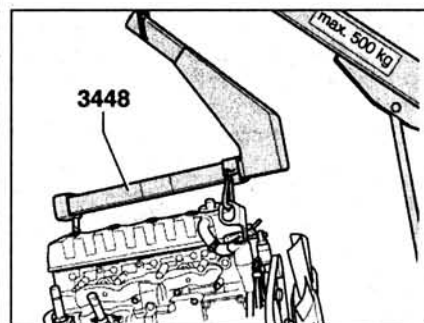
Снятие двигателя с помощью подъемника 3448.
